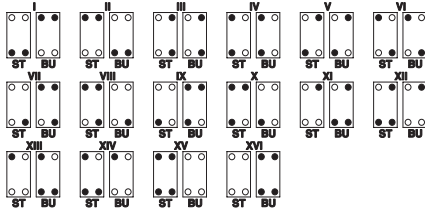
Механический ключ из втулки и штифта для корпусов с одной контактной вставкой
